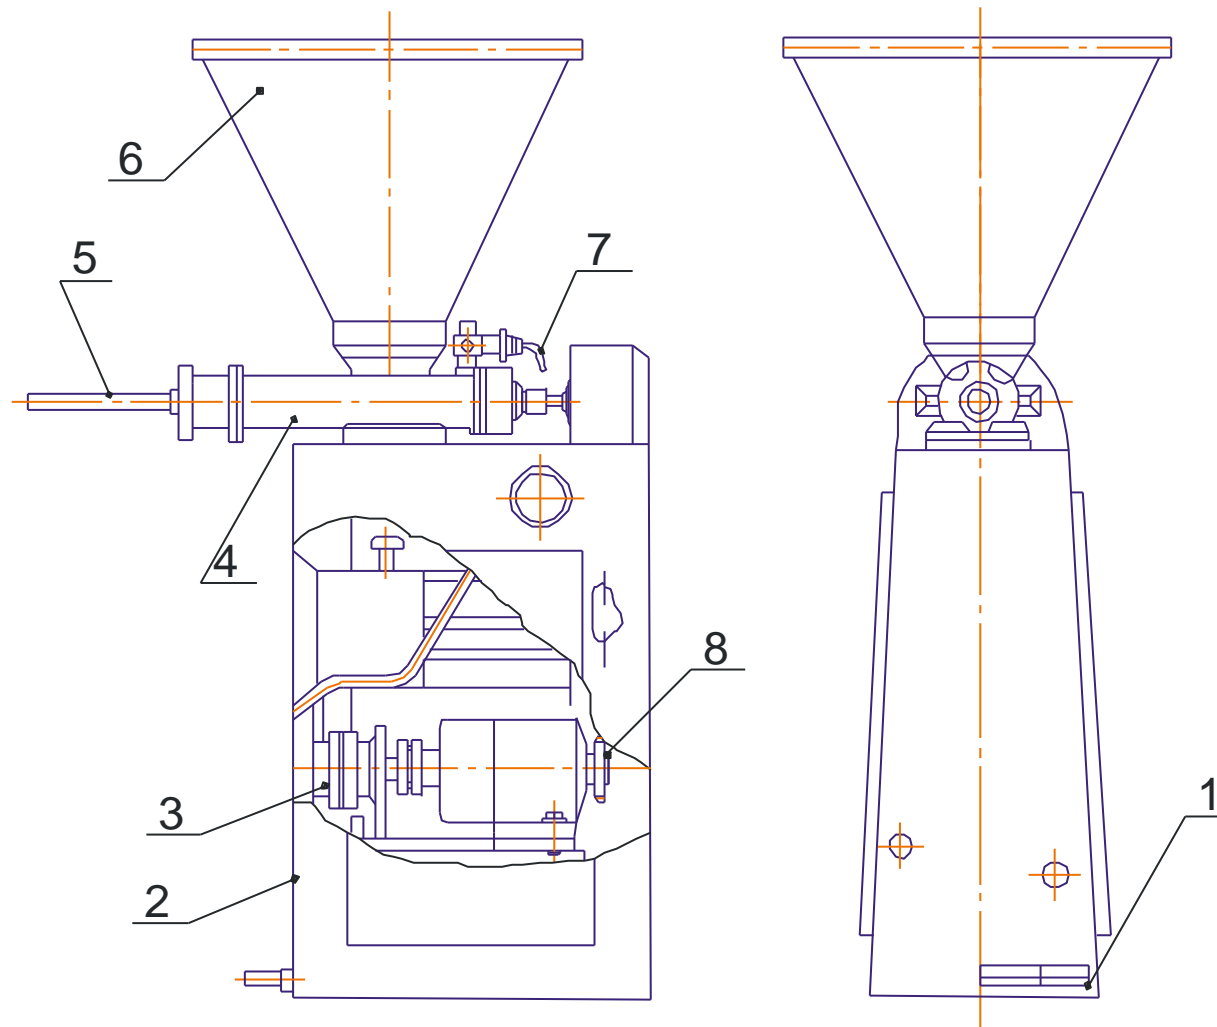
Двухцевочный вакуумный шприц ФШ2-ЛМ:
